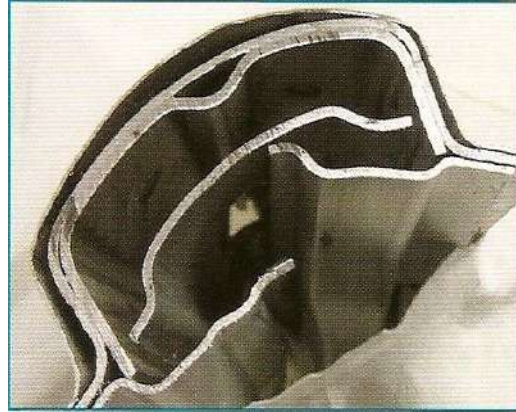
Secção de coluna B. Fonte Holmatro.
